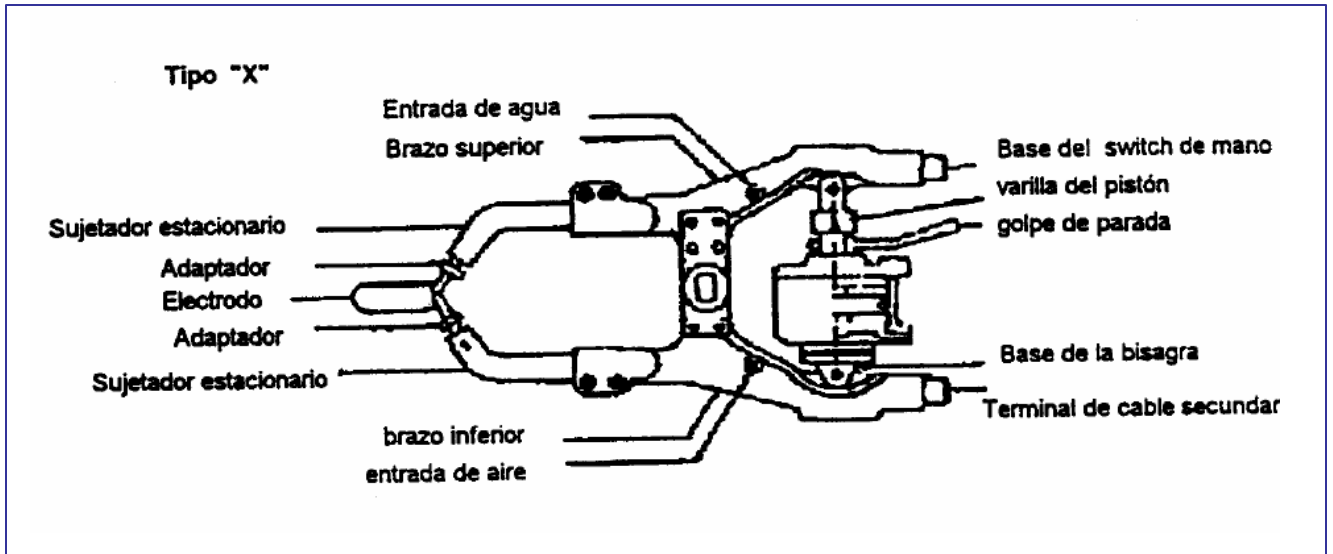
Pistola de soldadura por electropunto tipo "X"
